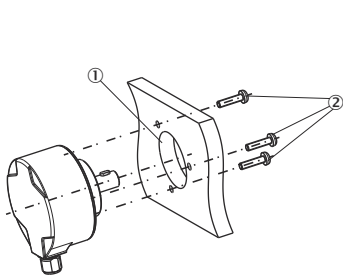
Anbau Klemmflansch über flanschseitige Gewindebohrungen
